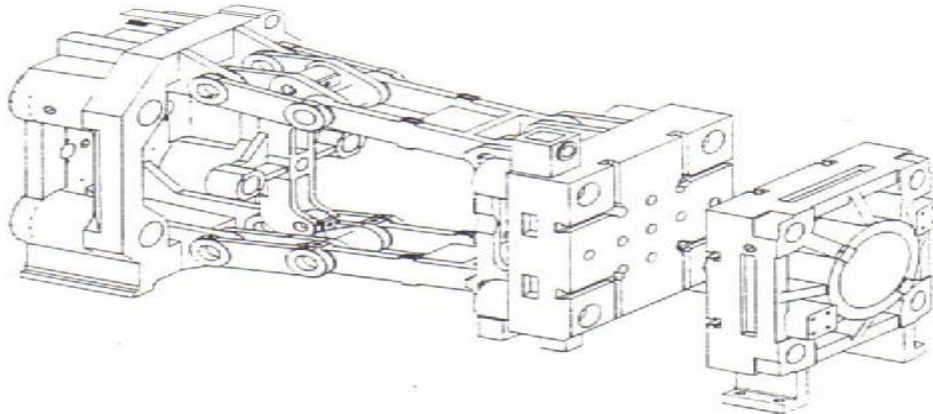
Sistema de rodilleras de una máquina de inyección.⁽¹⁰⁾
